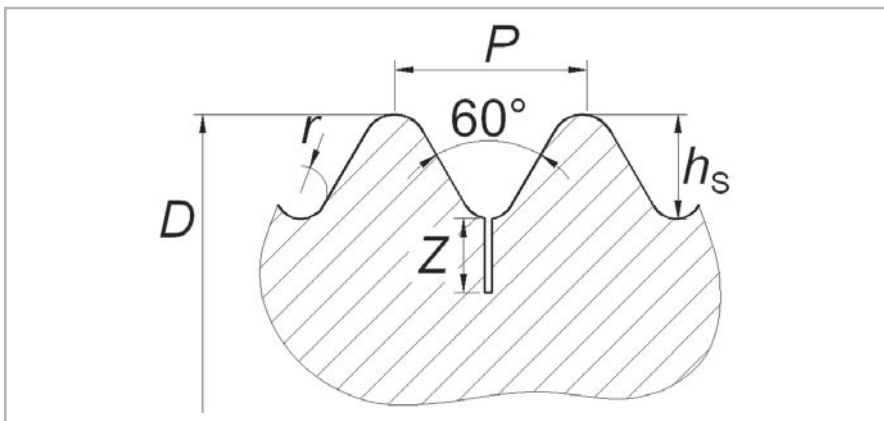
Эскиз профиля резьбы. P – шаг резьбы, h_s – высота профиля резьбы, r – радиус скругления впадины резьбы, Z – глубина трещины во впадине резьбы
